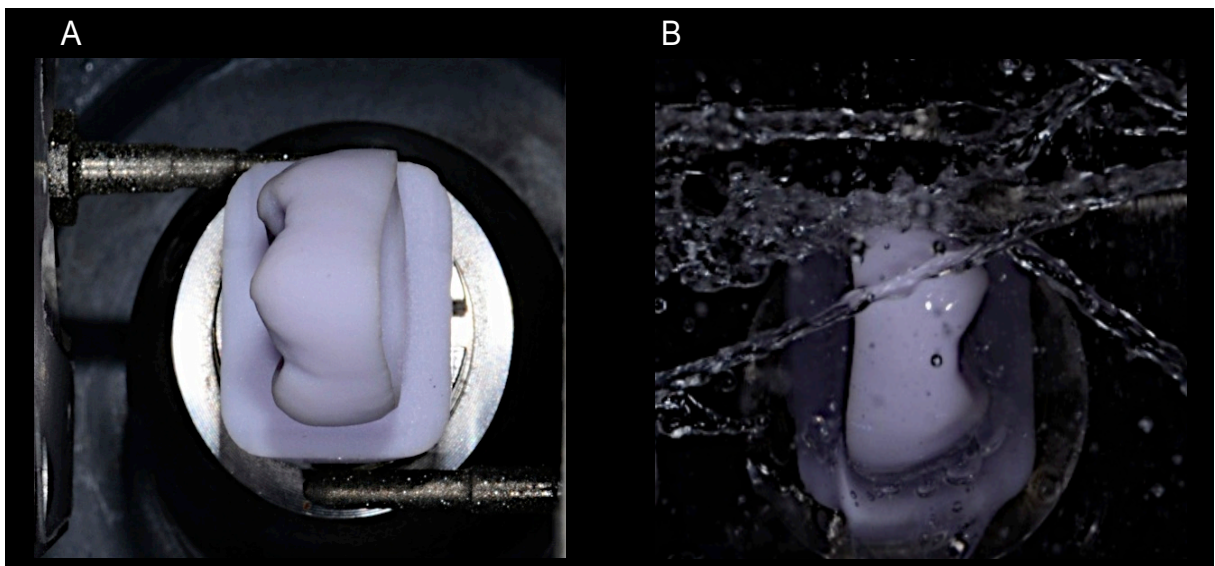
Visualização da fresagem de um bloco de IPS e.max CAD; (A) Visualização da ponta diamantada cilíndrica Step Bur 12S e ponta diamantada Cylinder Pointed Bur 12S; (B) Processo de usinagem, fresando um bloco de IPS e.max CAD sob constante e abundante refrigeração com jatos de água.
